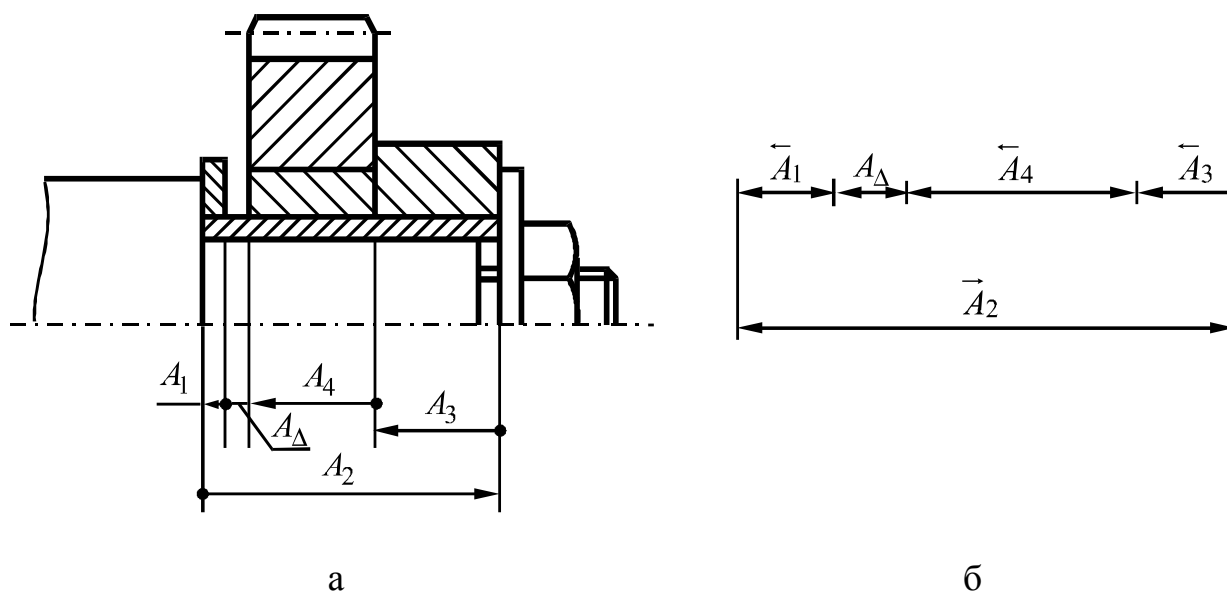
Конструкция узла крепления промежуточного зубчатого колеса:
